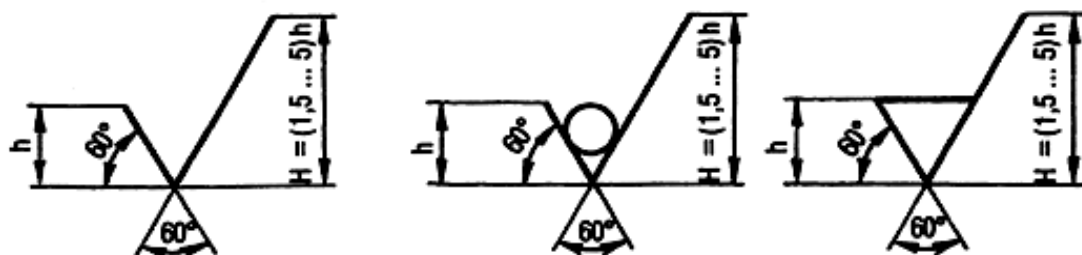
Знаки, применяемые для обозначения шероховатости
